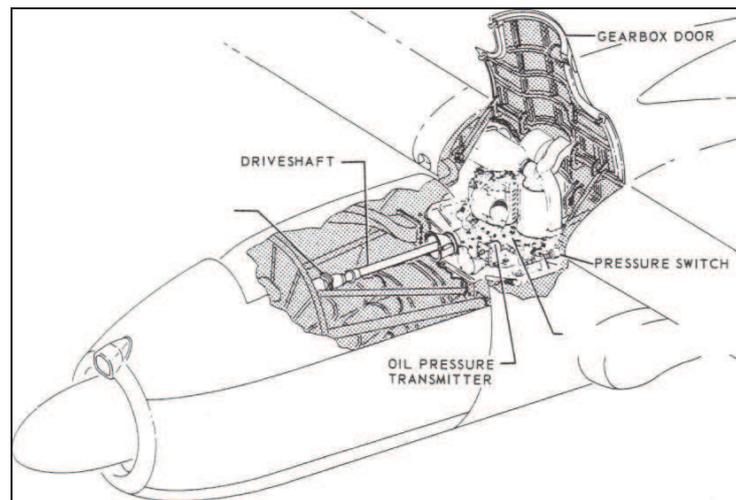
Instalación de los accesorios de la caja de engranajes
